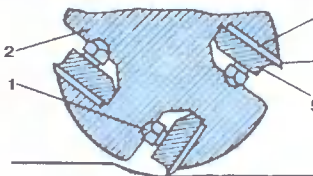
Барабан электрорубанка: 1 — крепежный болт, 2 — барабан, 3 — нож, 4 — режущая кромка ножа, 5 — прижимная планка.
